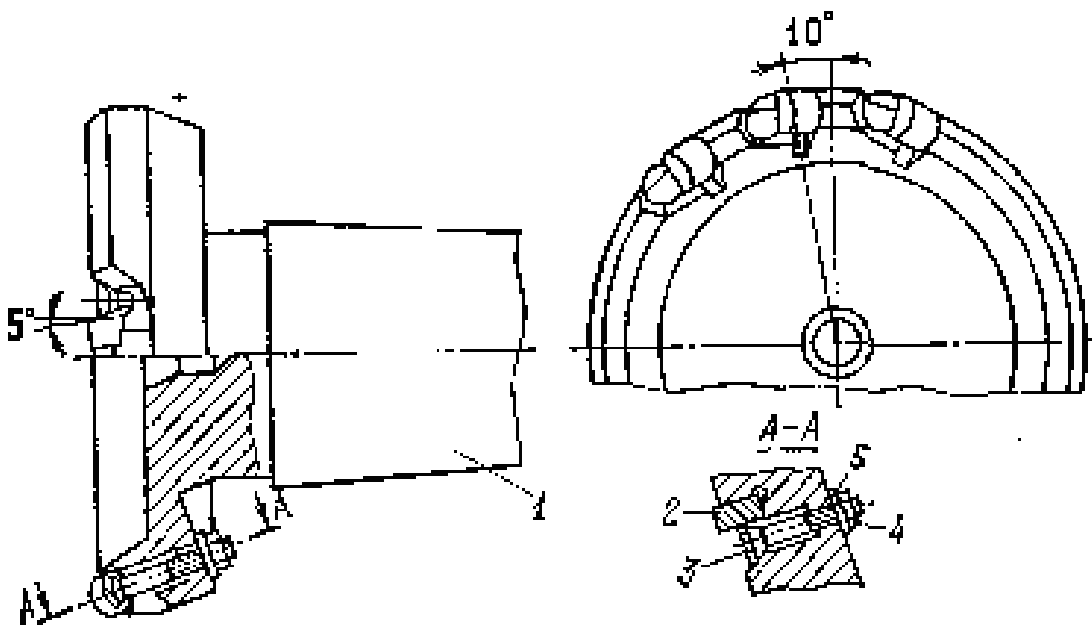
Торцево-кінцева фреза з механічним кріпленням круглих пластин з композиту
